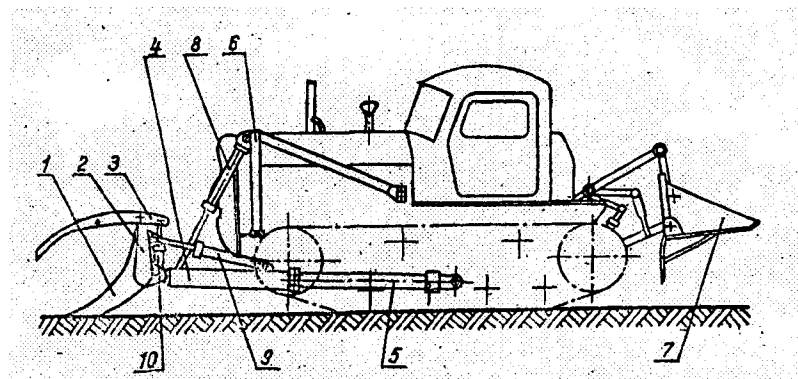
Корчеватель КПТ-75 (конструкция ЦНИИМЭСХ):
